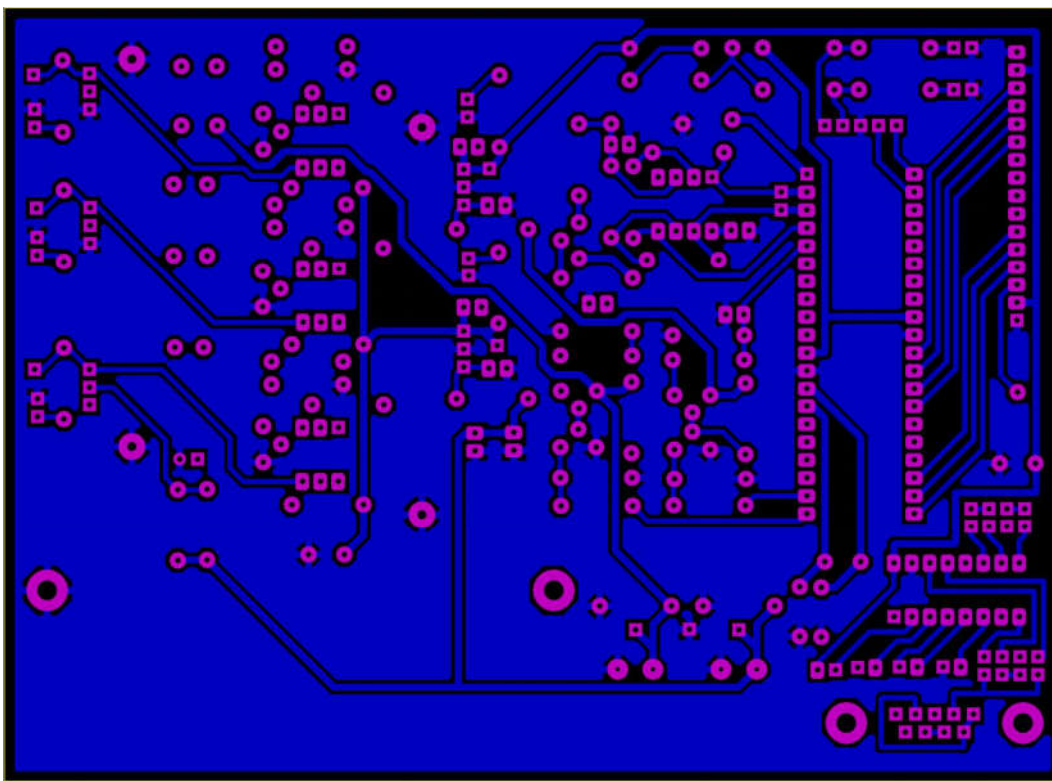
Face arrière de la carte électronique du régulateur de charge
